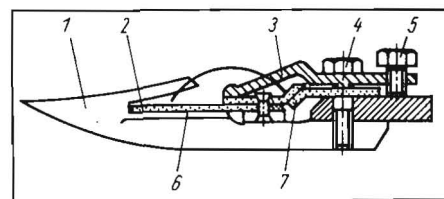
Schnitt durch einen modernen Fingermähbalken:
